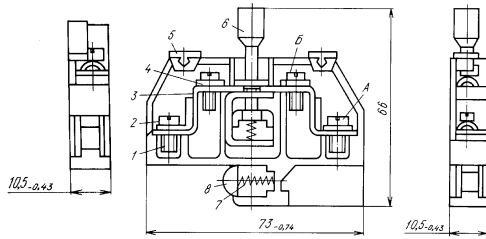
Габаритные, установочные и присоединительные размеры измерительных зажимов
